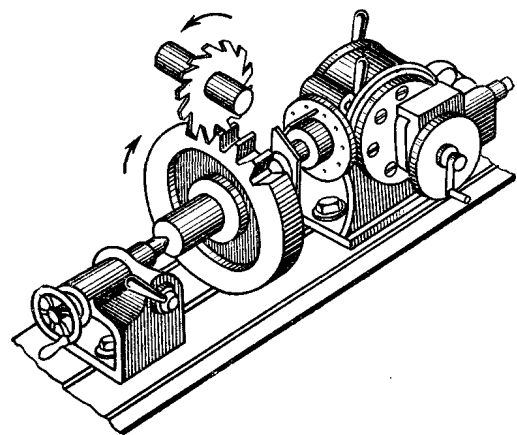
Схема нарізання зубчастих коліс дисковими фрезами
